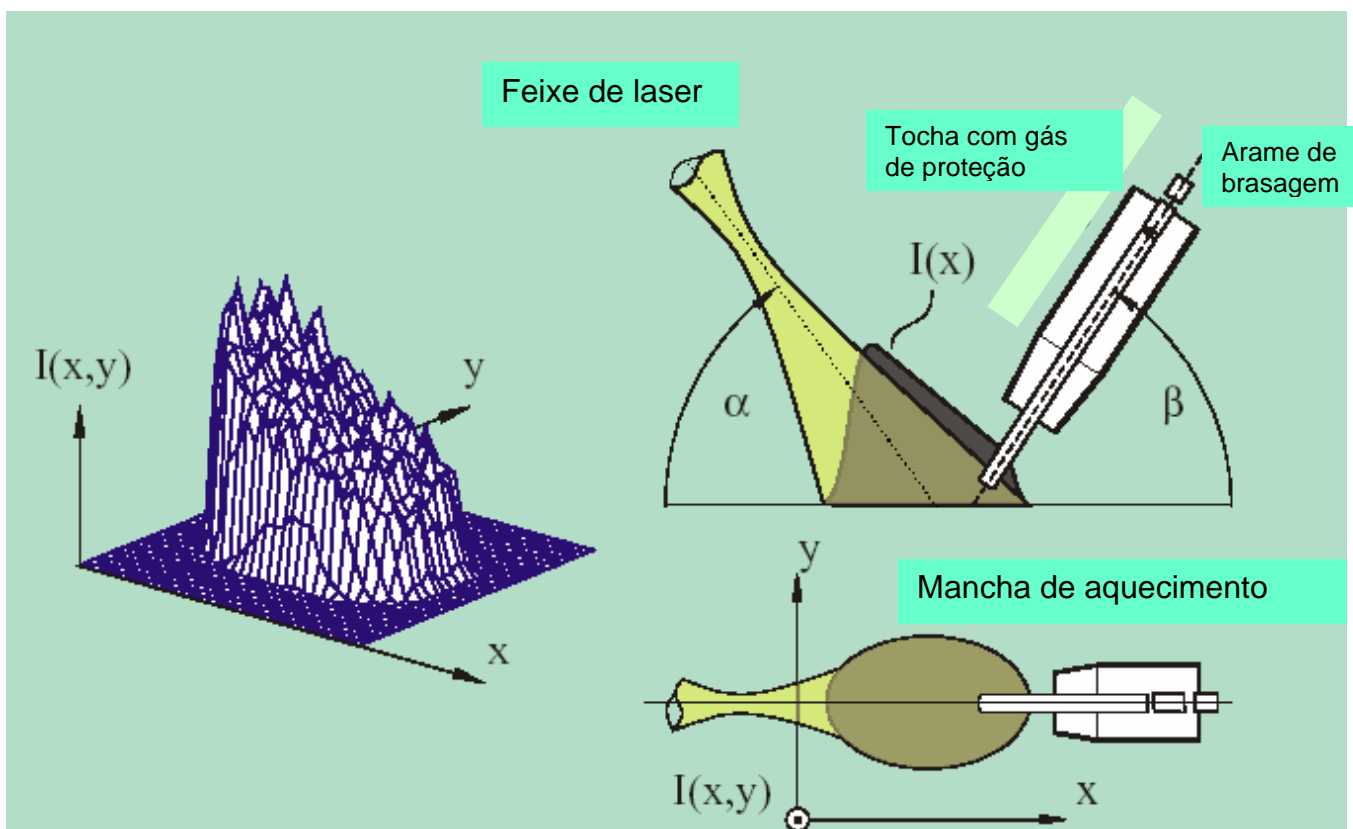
Pré-aquecimento direto do arame de brasagem na brasagem com feixe de laser com a técnica de feixe único.
